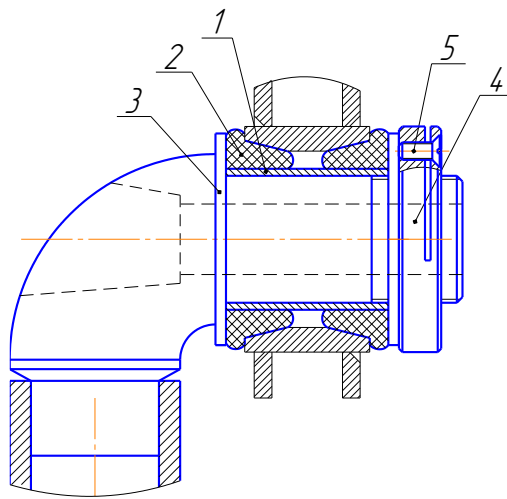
Конструкція шарнірного вузла з'єднання подовгастого важеля підвіски з рамою причепа
